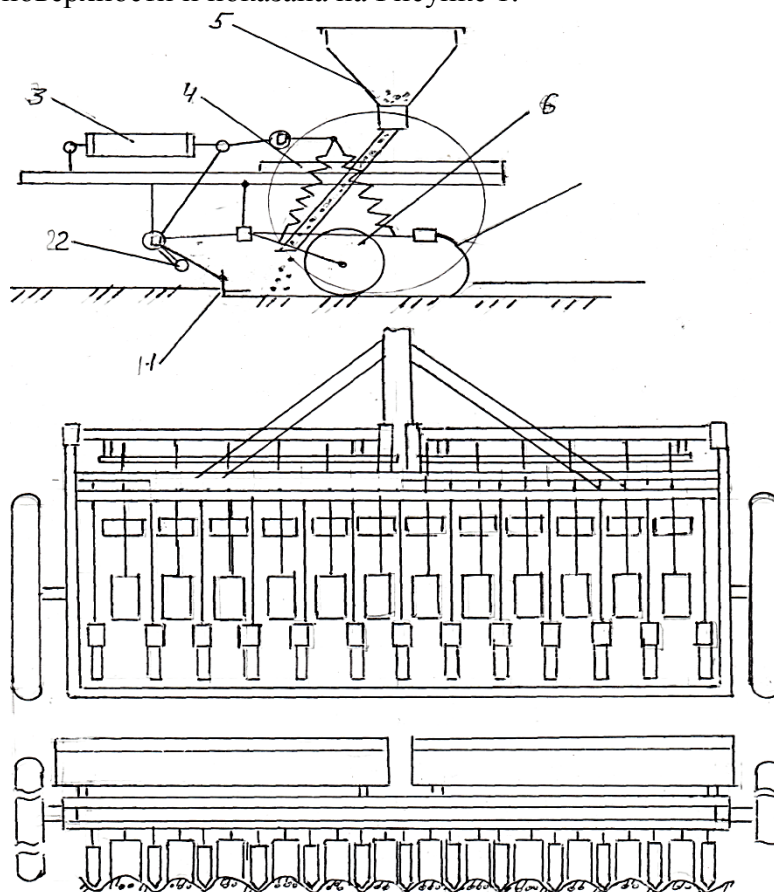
Сеялка зерновая гребне-катковая СЗГК-3,6У: 1 — приспособление для формирования семенного ложа, 2 — устройство для перевода приспособления в транспортное положение, 3 — гидроцилиндр, 4 — рама, 5 — зернотуковой ящик, 6 — каток, 7 — заделывающая лапа.
